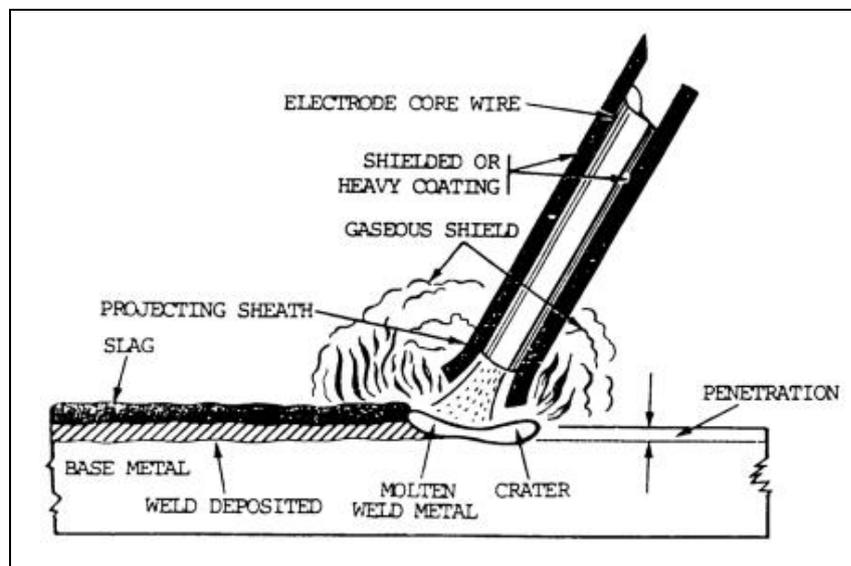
Soldadura producida por arco eléctrico
